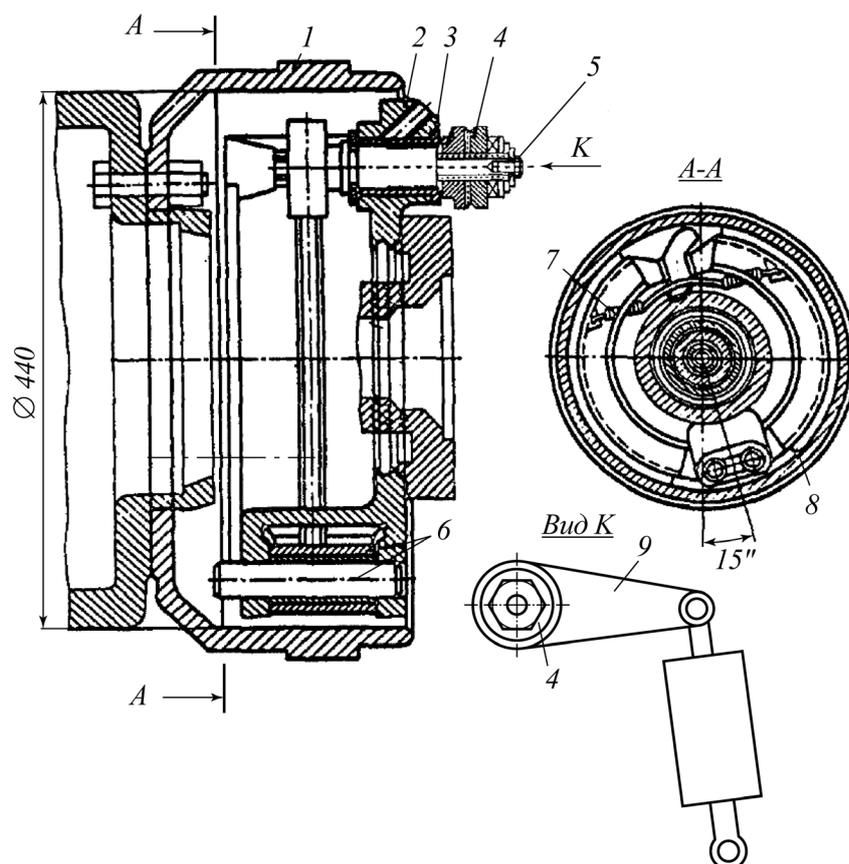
Рабочий тормоз самоходного вагона: 1 – барабан тормозной; 2 – суппорт тормоза; 3 – втулка суппорта; 4 – шестерня зубчатая регулировочного рычага; 5 – кулак разжимной; 6 – оси тормозных колодок; 7 – пружины; 8 – накладки фрикционные; 9 – рычаг регулировочный
